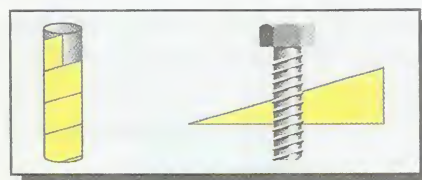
A cartolina é enrolada no cilindro produzindo um efeito semelhante ao parafuso.
